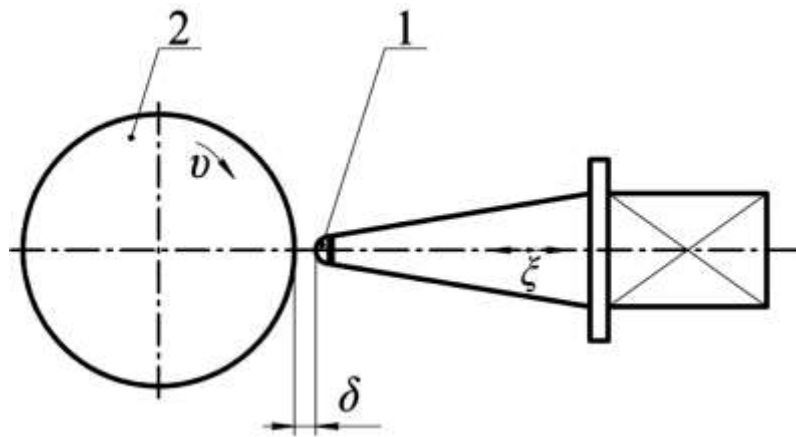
Схема ППД з ультразвуком: 1 – інструмент; 2 – деталь
